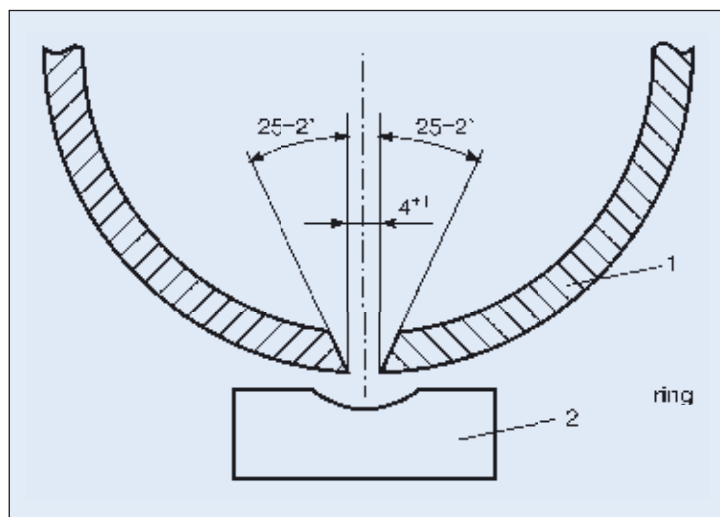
Схема сварки колец спрямляющего аппарата: 1 — кольцо, 2 — медная формирующая подкладка
